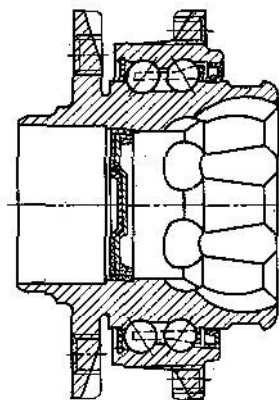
У подшипников четвертого поколения шарнир равных угловых скоростей включен в конструкцию опорного узла колеса. Ступица колеса, корпус шарнира и внутреннее кольцо радиально-упорного шарикоподшипника объединены в одну деталь. Наружное кольцо имеет фланец с резьбовыми отверстиями для крепления к опоре подшипника колеса. Изображенная конструкция разработана для передних ведущих колес
